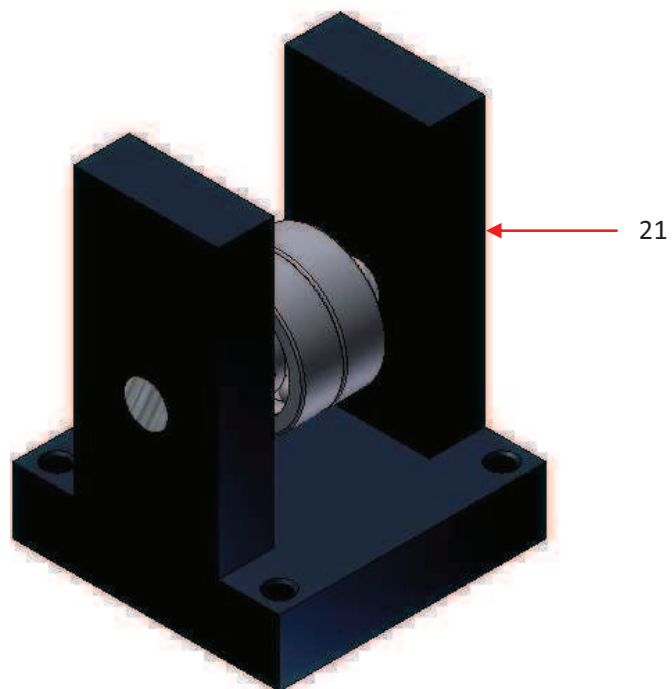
Apoyo con rodamientos para columna sin instrumentación.
